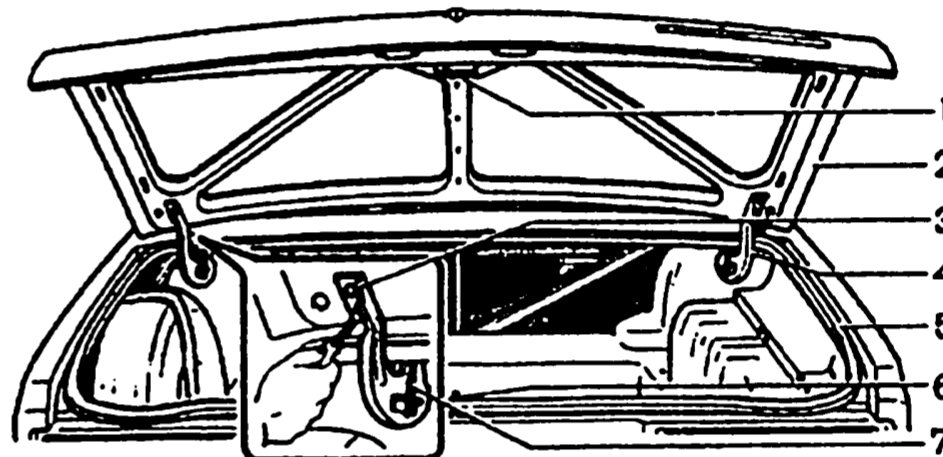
Крышка багажника: 1 - замок; 2 - крышка багажника; 3 - гайка; 4 - петля; 5 - уплотнитель; 6 - фиксатор; 7 - торсион
